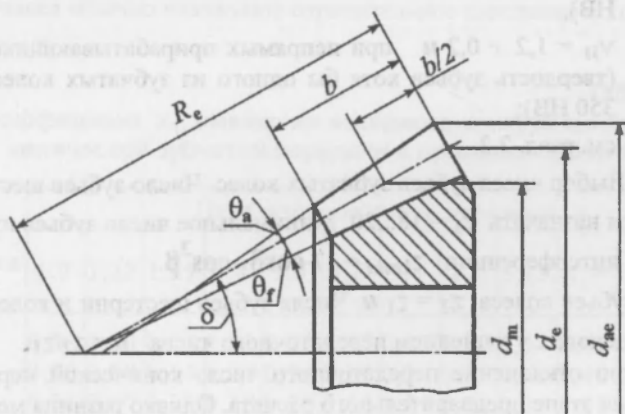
Геометрические параметры конического зубчатого колеса (форма зуба I)
